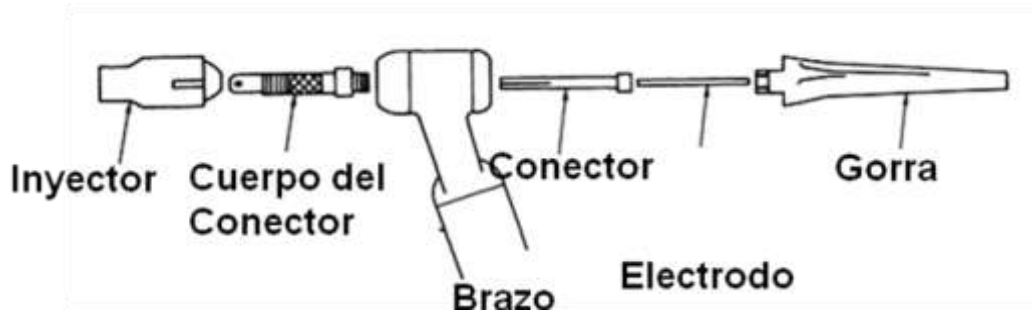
Principales Componentes de la Antorcha para soldadura TIG
